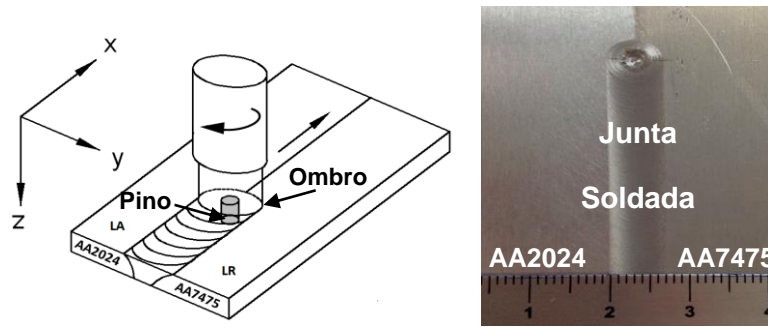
(a) Esquema dos materiais dissimilares unidos pelo processo FSW, indicando o sentido da rotação do pino de soldagem, o lado do avanço (LA) e do retrocesso (LR); (b) Macroscopia da chapa soldada.
